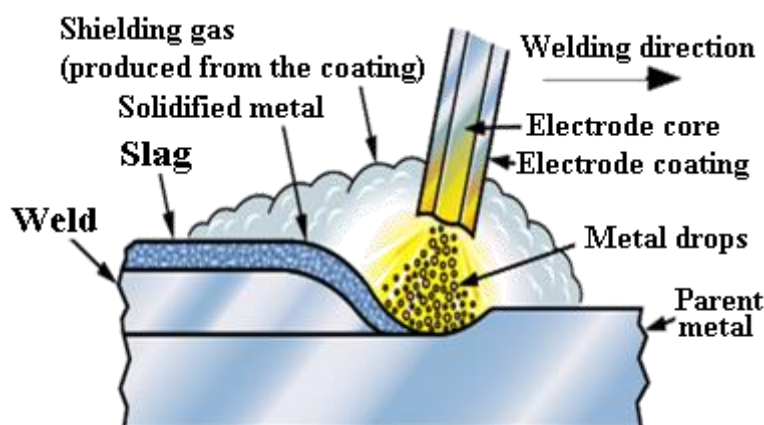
Processo de Soldadura com Eletrodo Revestido.
